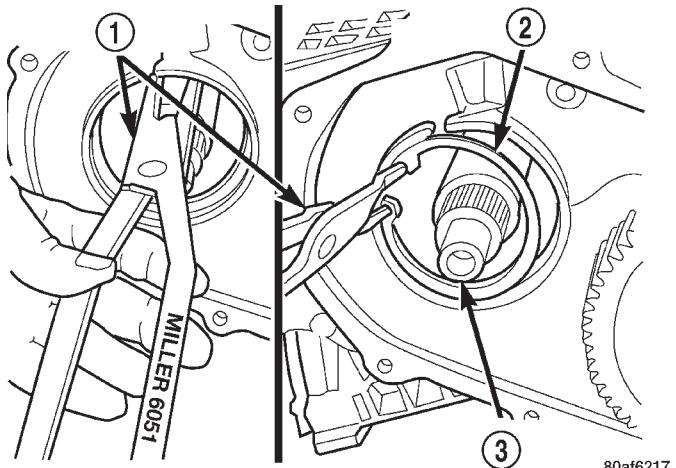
Desmontaje del cono del cojinete del engranaje de transferencia
